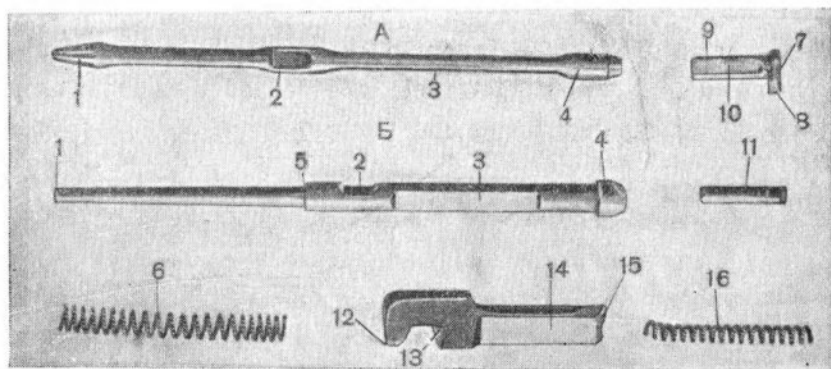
Ударники двух вариантов, чека и шпилька (2—7) ударников, выбрасыватель (2—3) и пружина выбрасывателя:
